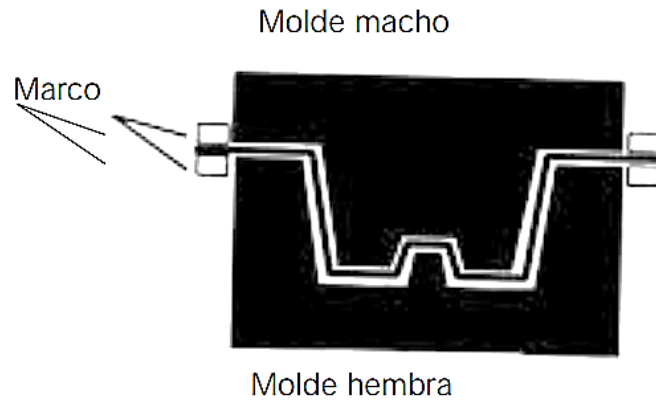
Termoformado mecánico con molde hembra y macho [48].
